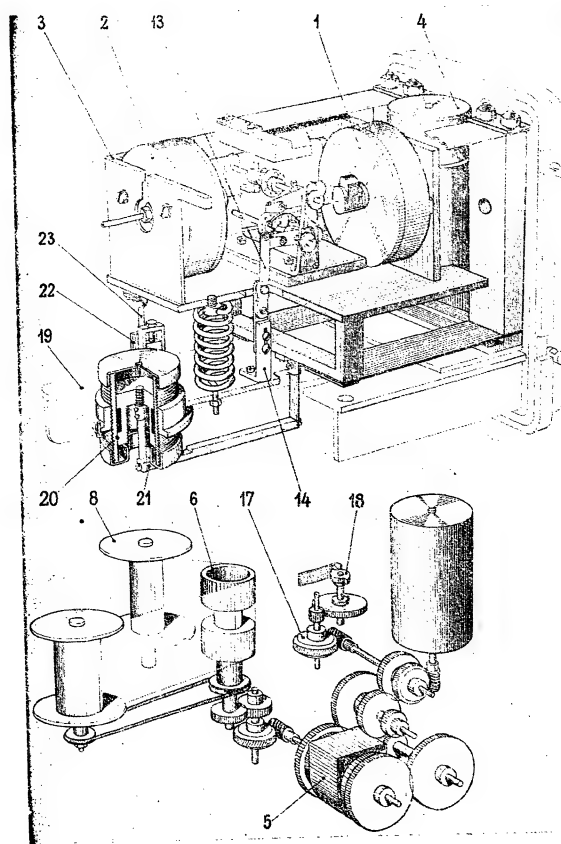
МЕХАНИЗМ ПРИБОРА (вид слева)
